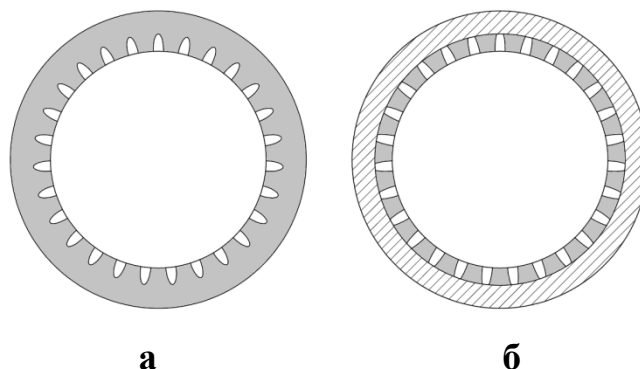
Схема гильзы двигателя в сечении: а – гильза из газара; б – кольцо из газара со сквозными порами запрессованное в монолитный цилиндр.
